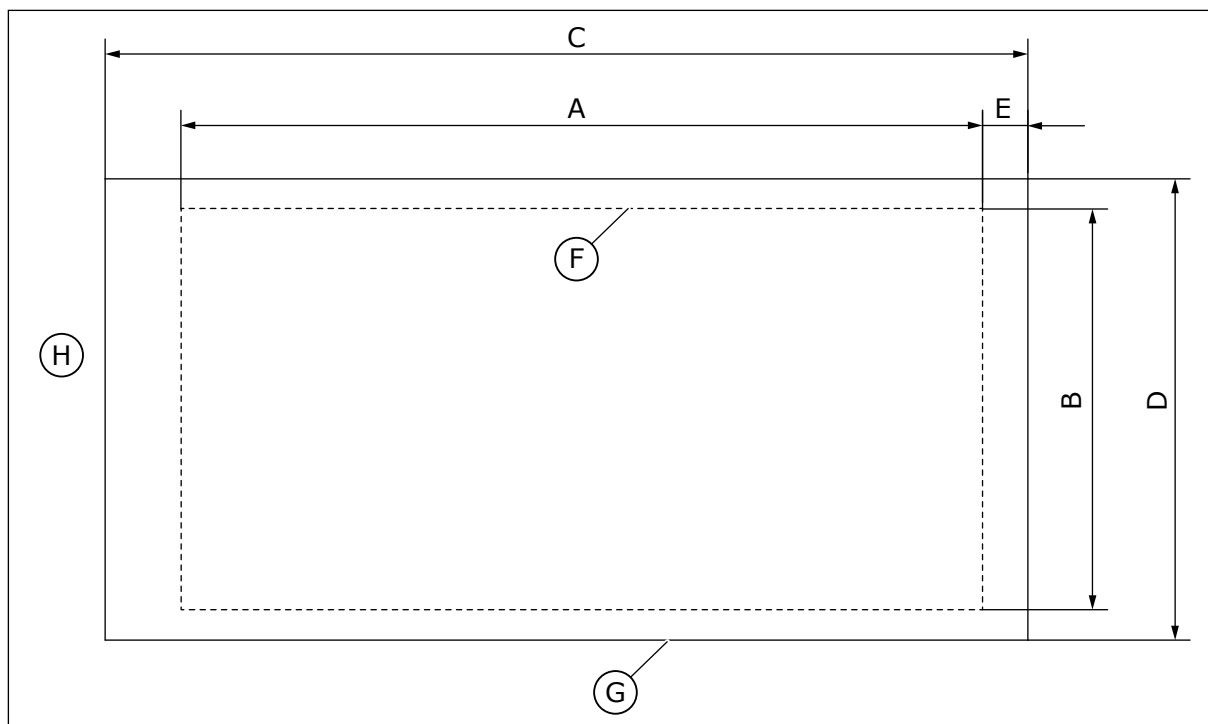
Dimensionerne af åbningen og grundrids af frekvensomformerer med flange
